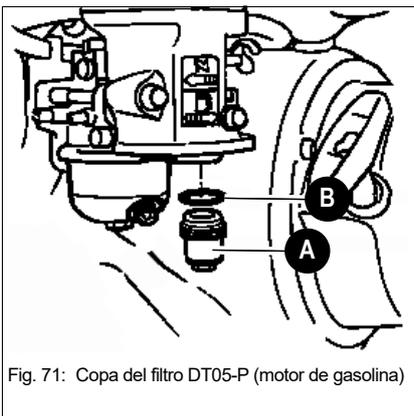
Copa del filtro DT05-P (motor de gasolina)
